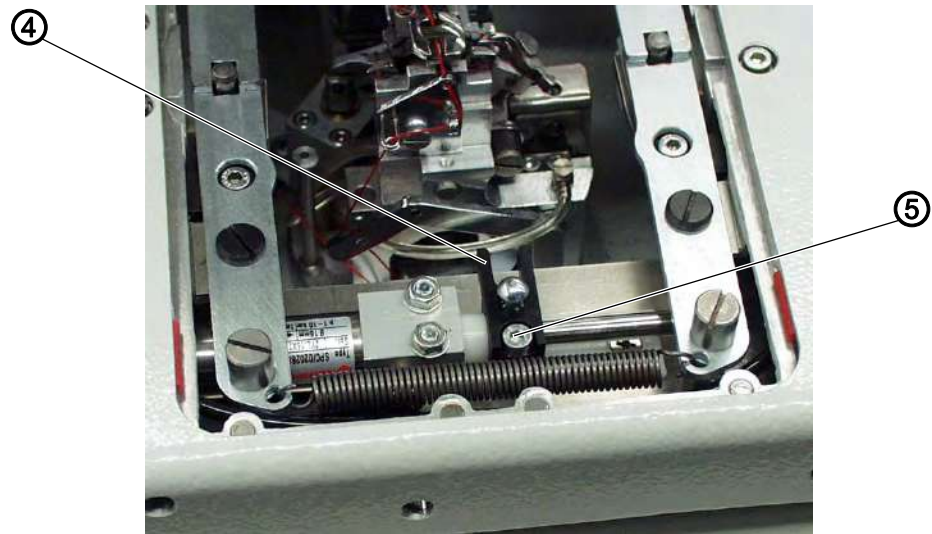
Короткая обрезка, настройка положения режущего механизма (2)
